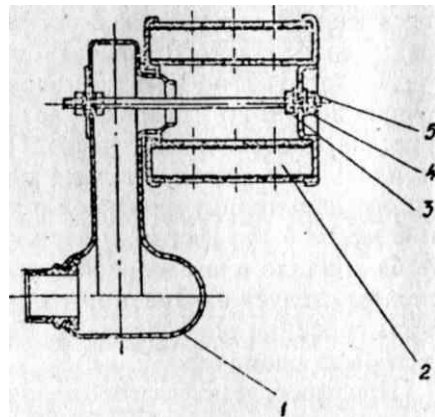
Схема установки воздушного фильтра мопеда "Верховина" с бумажным фильтрующим элементом: 1 - ресивер; 2 - шпилька; 3 - корпус; 4 - бумажный фильтрующий элемент; 5 - гайка
